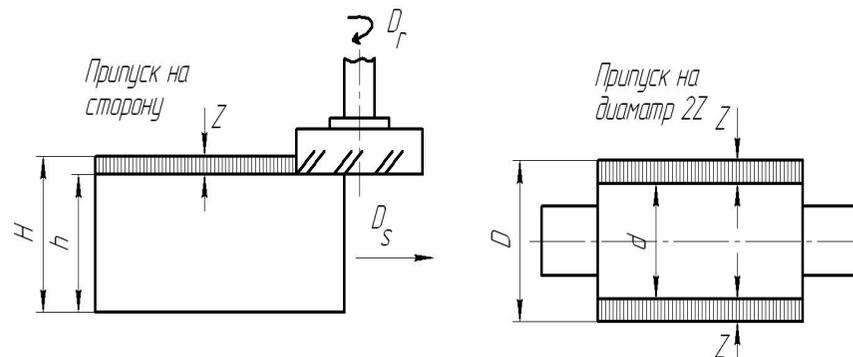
Обозначение припуска при обработке плоских и цилиндрических поверхностей: H - промежуточный размер заготовки; Z – припуск на размер h (припуск на сторону); $2Z$ – припуск на диаметр d .
